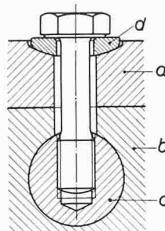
Ausführungsform für eine häufig zu lösende Stiftschraube bei Leichtmetallteilen.
